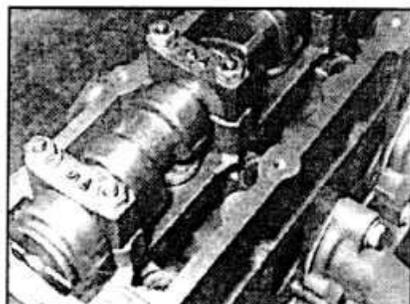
Е.23. Обозначение направления установки и нумерация крышек подшипников распределительного вала.
